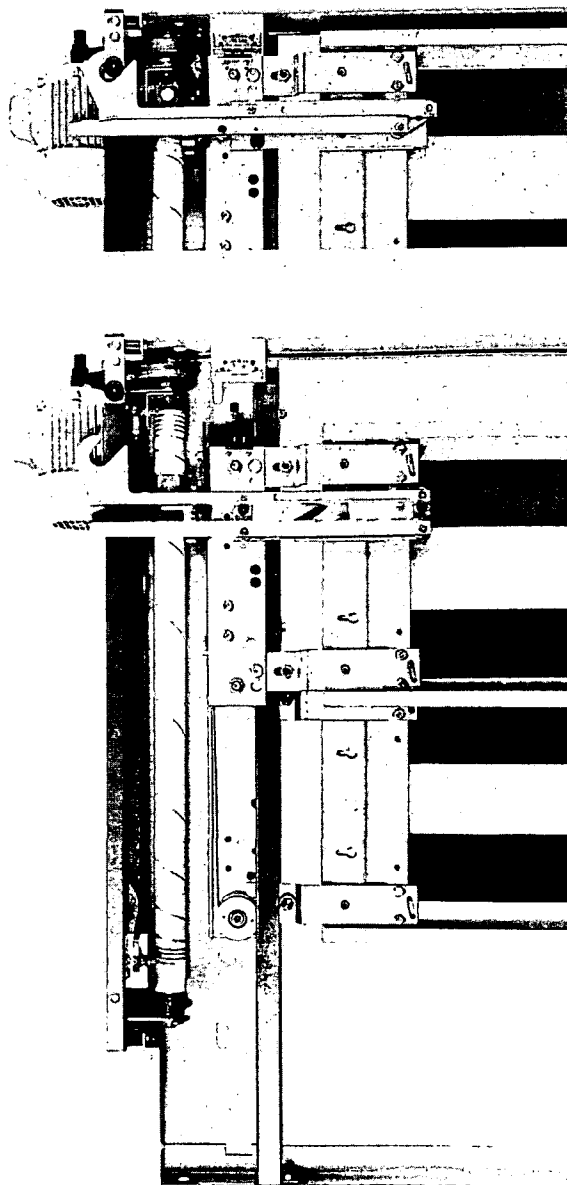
Винтовой привод двери (F.X.Meiller)
